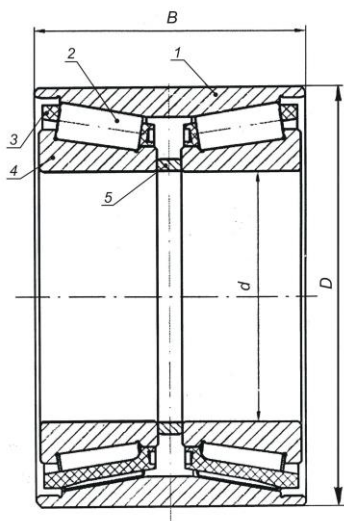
Роликовый конический двухрядный подшипник
